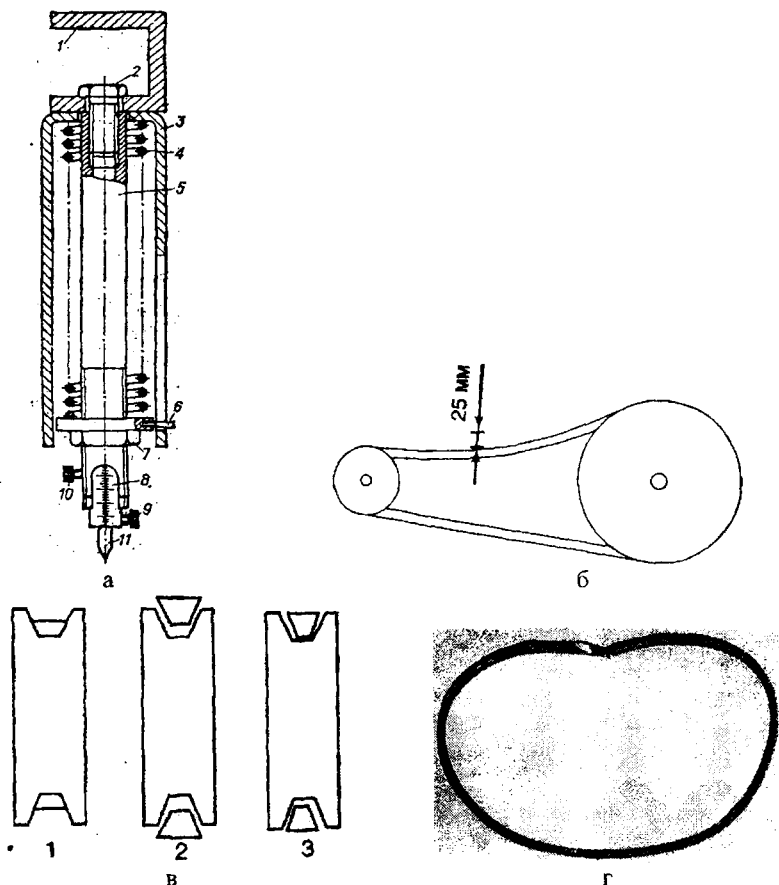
Натяжение ремня в шкиве:
